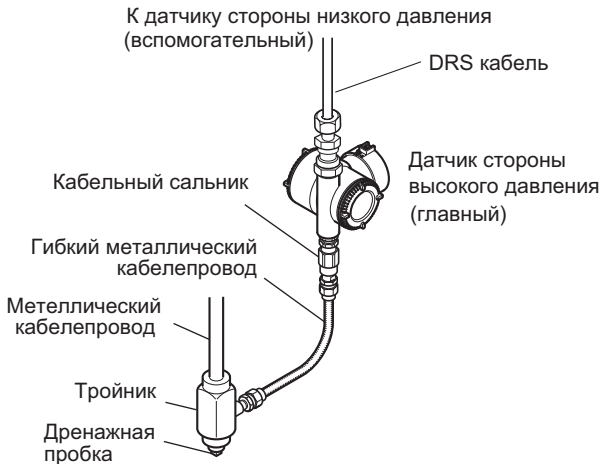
Типовая проводка с использованием кабельного сальника
